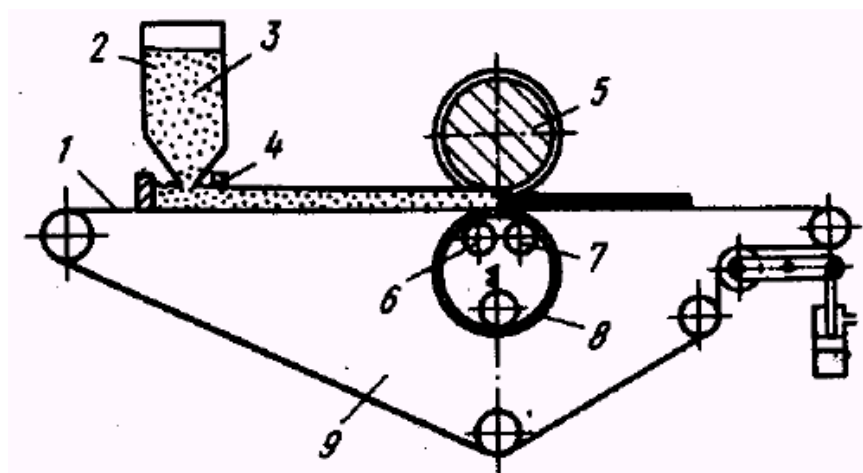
Схема прокатки порошка с использованием прокатного стана и подающей гибкой ленты: 1 – лента; 2 – бункерное устройство; 3 – металлический порошок; 4 – выравнивающее устройство; 5 – верхний валок с буртами; 6 и 7 – прижимные ролики; 8 – нижний валок
